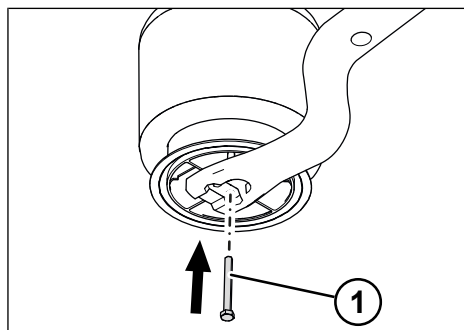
Fixer la vis de fixation de la membrane de suspension pneumatique
